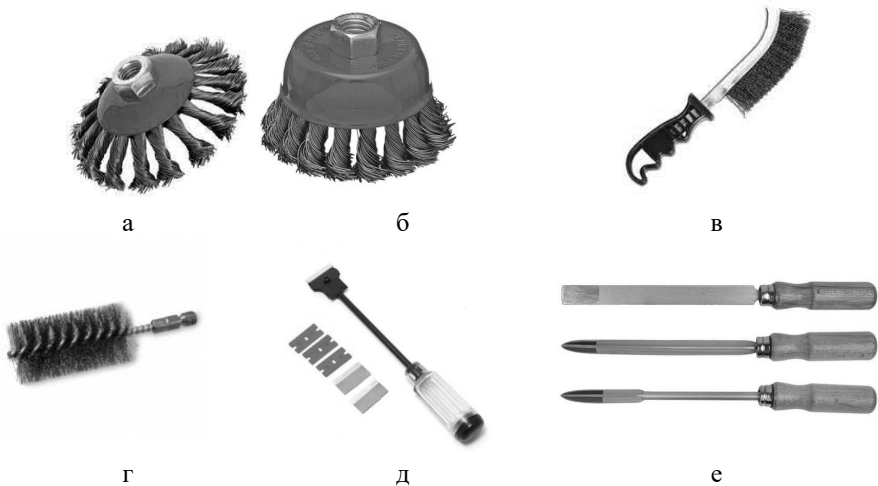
Інструмент для механічного та ручного очищення поверхонь:
